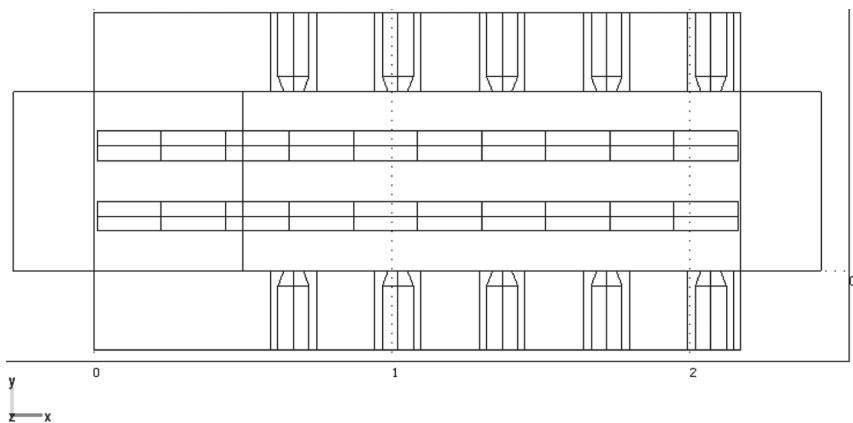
Чертеж нагревательной печи скоростного струйного нагрева металла (вид сверху)
